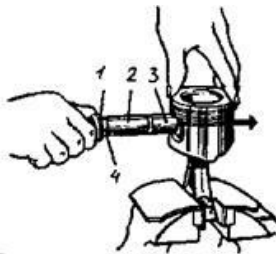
Запрессовка поршневого пальца двигателей ВАЗ в верхнюю головку шатуна с помощью оправки: 1 – рукоятка оправки с упорным буртиком; 2 – поршневой палец; 3 – направляющая; 4 – дистанционное кольцо
